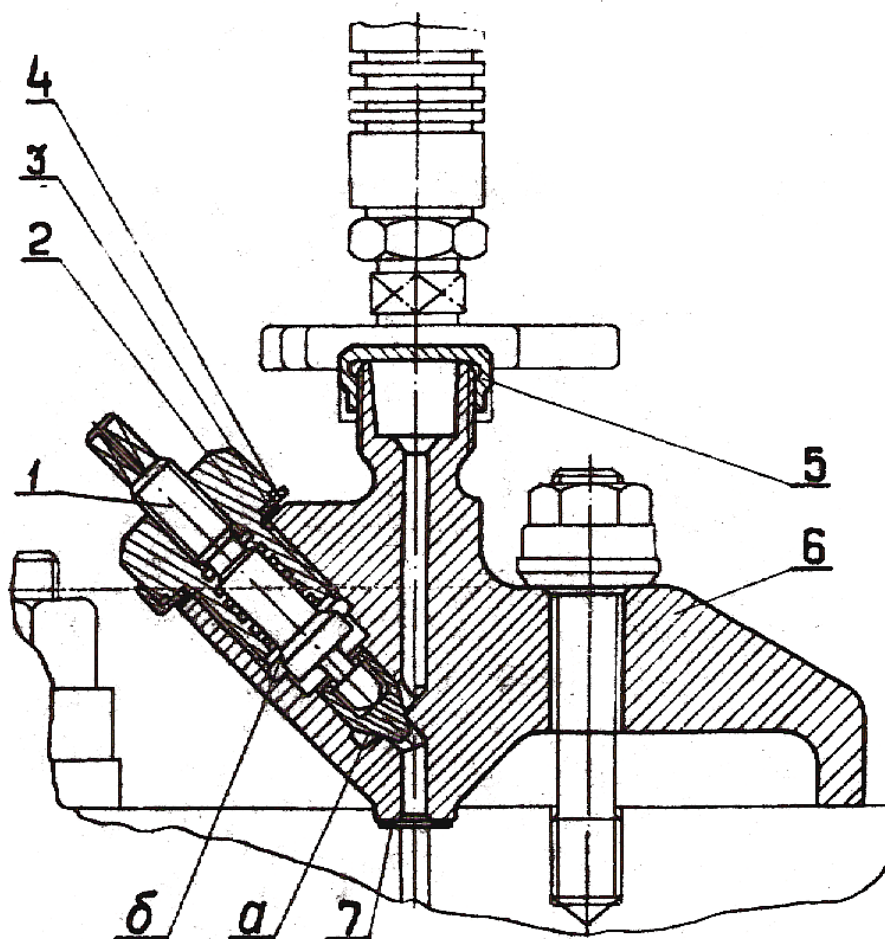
Кран индикаторный: 1 – шпindelь; 2 – штуцер; 3, 7 – прокладка; 4 – замочная пластина; 5 – колпачок; 6 – корпус крана; а, б – уплотняющие конусы
